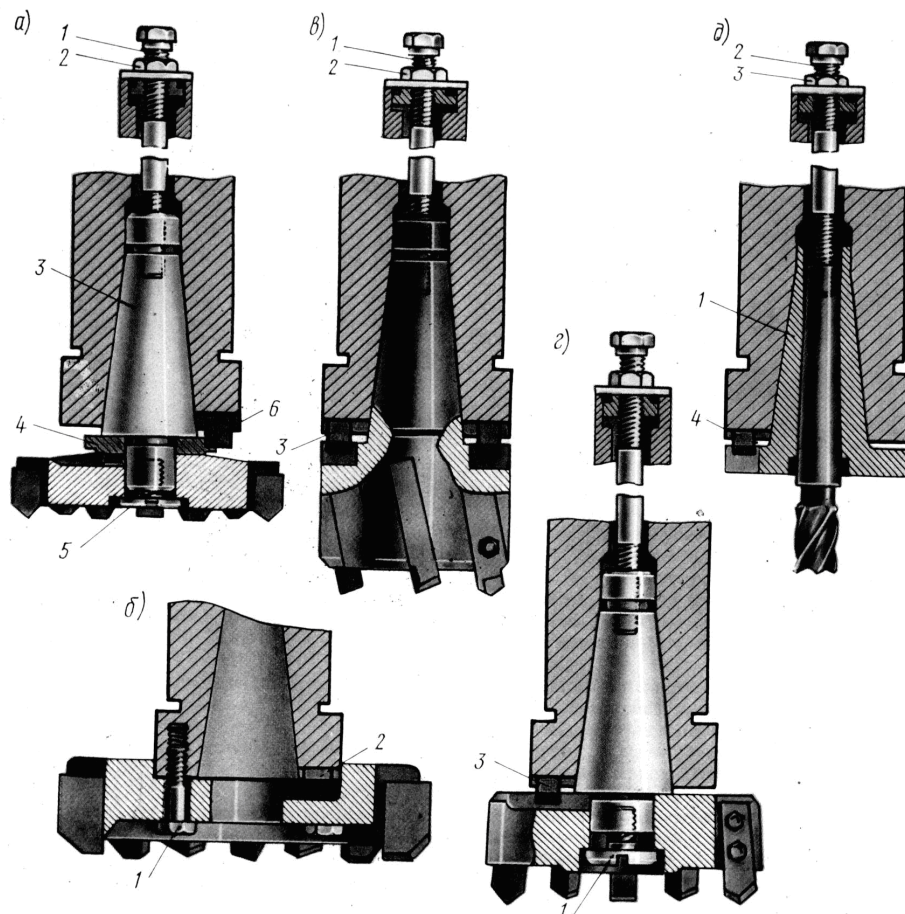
Закріплення фрез при роботі торцевими фрезами на вертикально-фрезерному верстаті
